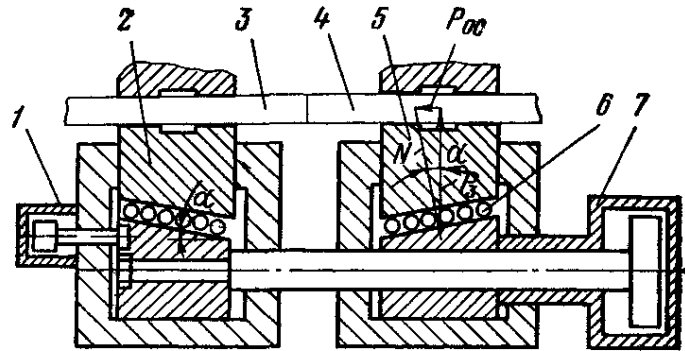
Зажимы с самозаклиниванием: 1 — цилиндр предварительного зажатия, 2, 5 — башмаки, 3, 4 — детали, 6 — опора качения, 7 — цилиндр осадки
